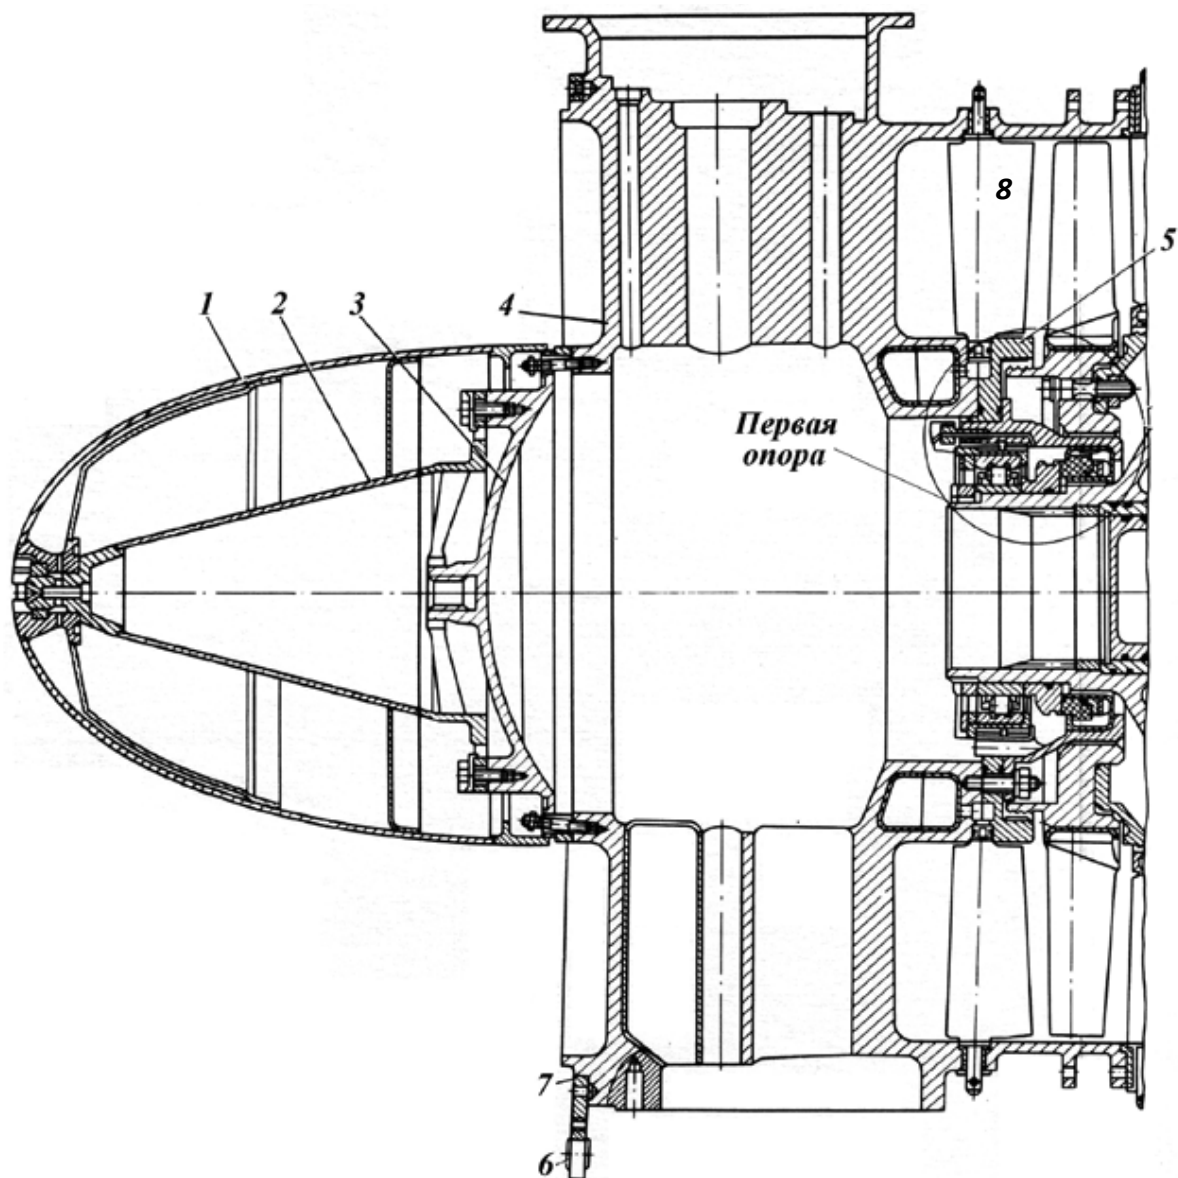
Разрез корпуса I опоры двигателя ТВ3-117: 1 – кок, 2 – конус, 3 – крышка, 4 – горизонтальная стойка, 5 – узел I опоры, 6 – шарнирное гнездо подвески двигателя, 7 – фланец корпуса I опоры, 8 – лопатка ВНА
